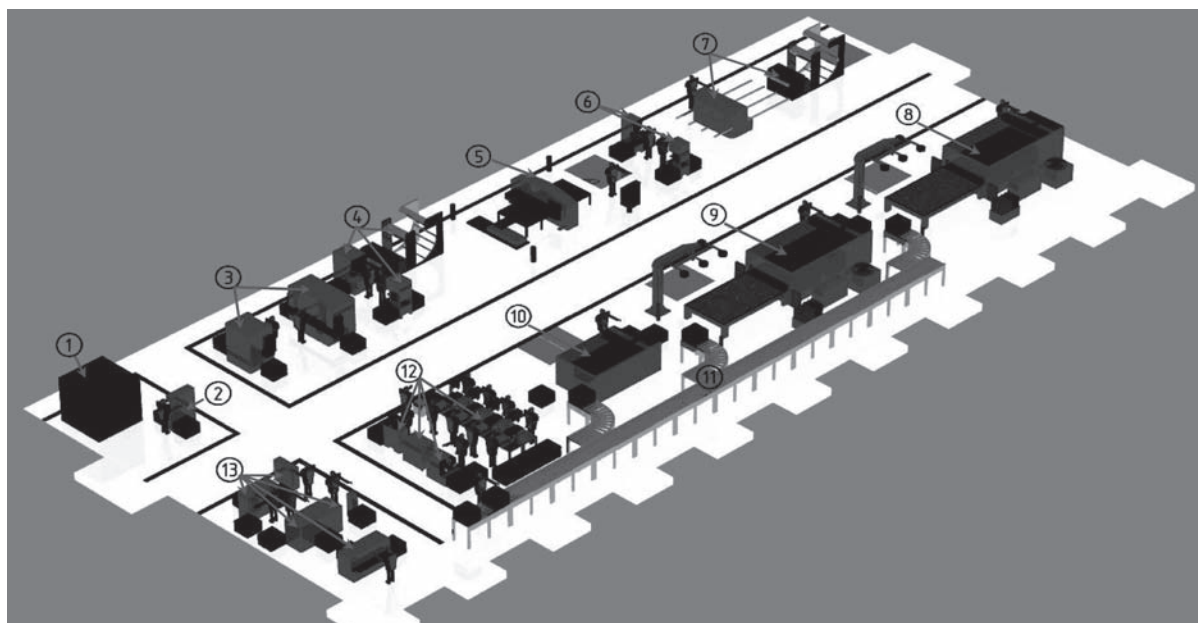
Фрагмент проекта цеха: 1 – склад для межоперационного хранения деталей и инструмента, 2 – машина точечной и рельефной сварки, 3 – участок прессов свободной гибки; 4, 6 – прессы для штамповки деталей из полос и ленты, 5 – КПП, 7 – ГН; 8, 9 – комплексы ЛР металлического листа, 10 – комплекс ЛР листов из неметаллов, 11 – рольганг для межоперационного транспортирования, 12 – оборудование для механообработки деталей из листа (снятие фасок, нарезание резьбы, фрезерование не сквозных пазов, токарная обработка и т.д.), 13 – участок зачистки деталей
